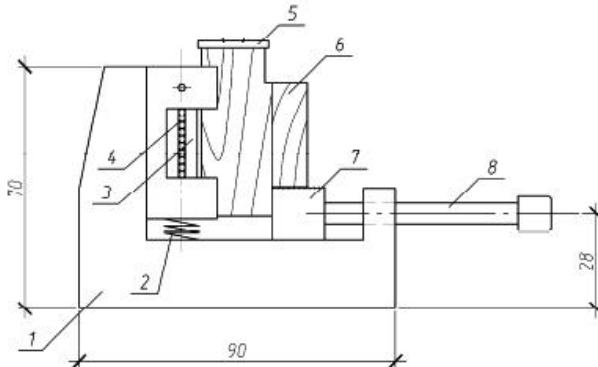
Приспособление для испытаний на скалывание:
